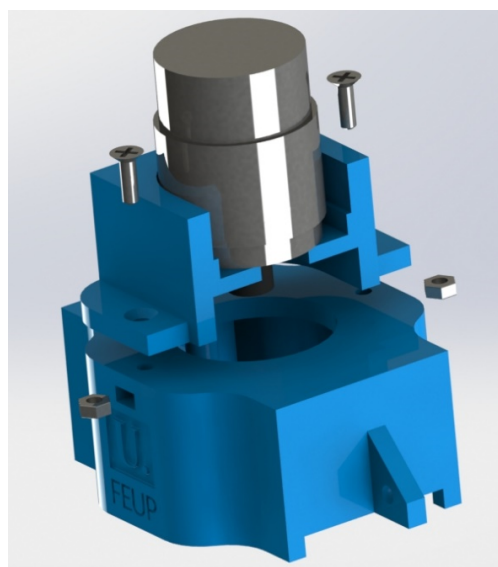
Vista explodida do sistema de fixação do suporte do motor à tampa do protótipo
